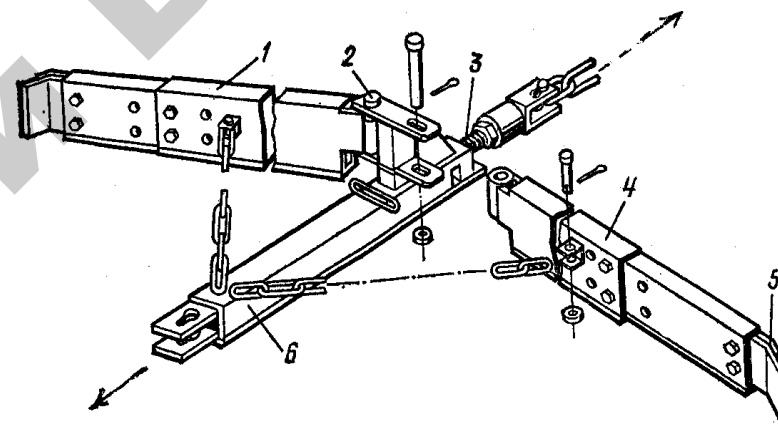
Складывающийся скрепер установки УС-Ф-170:
